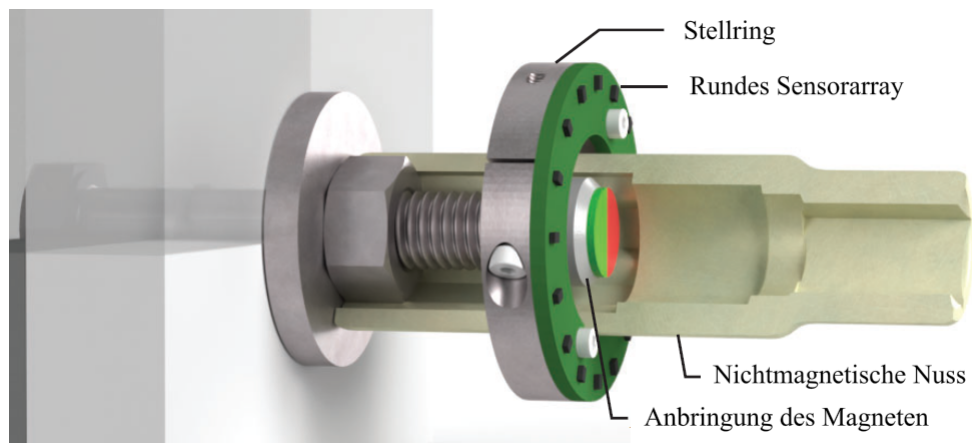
Vorschlag für Design des Schraubwerkzeuges aus "Magnetic Sensor Array for Determining the Assembly Torsion and Preload of a Bolted Joint"[8]
